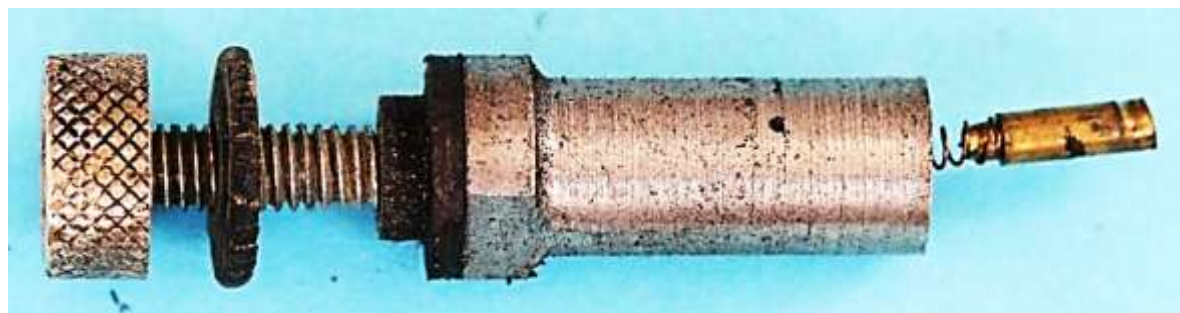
Kabelanschlussbolzen mit Bürstenhalter
